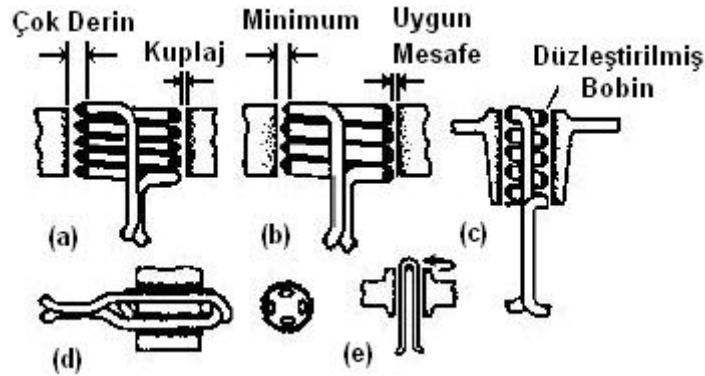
Bölgesel ısıtma için değişik şekilli bobinler
